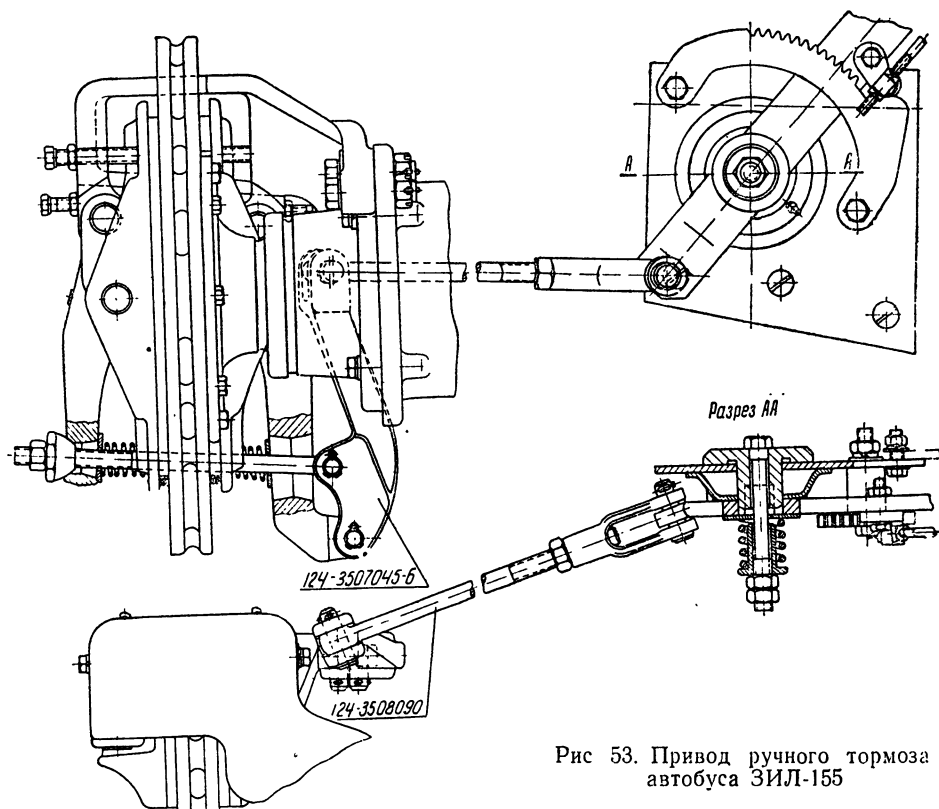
Привод ручного тормоза автобуса ЗИЛ-155
